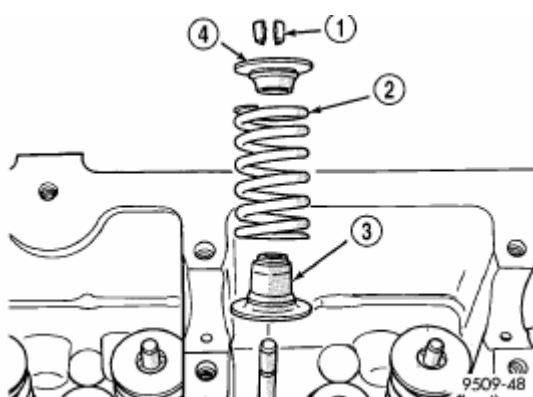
Уплотнение штока клапана/Седло клапанной пружины – типовой вид.
